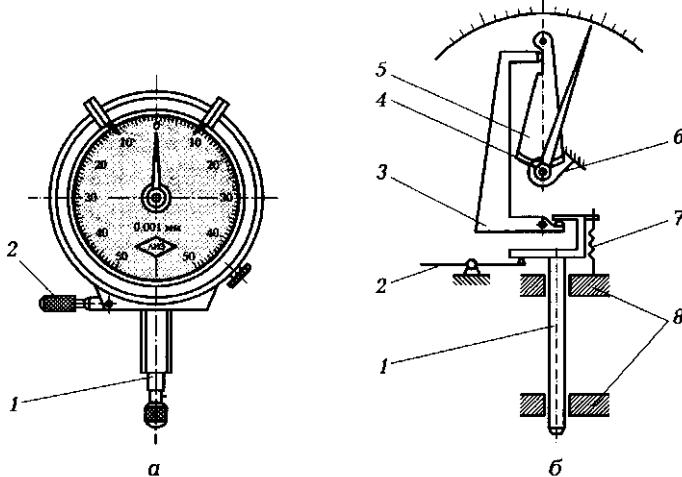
Рычажно-зубчатая измерительная головка [а] и ее схема [б]:
